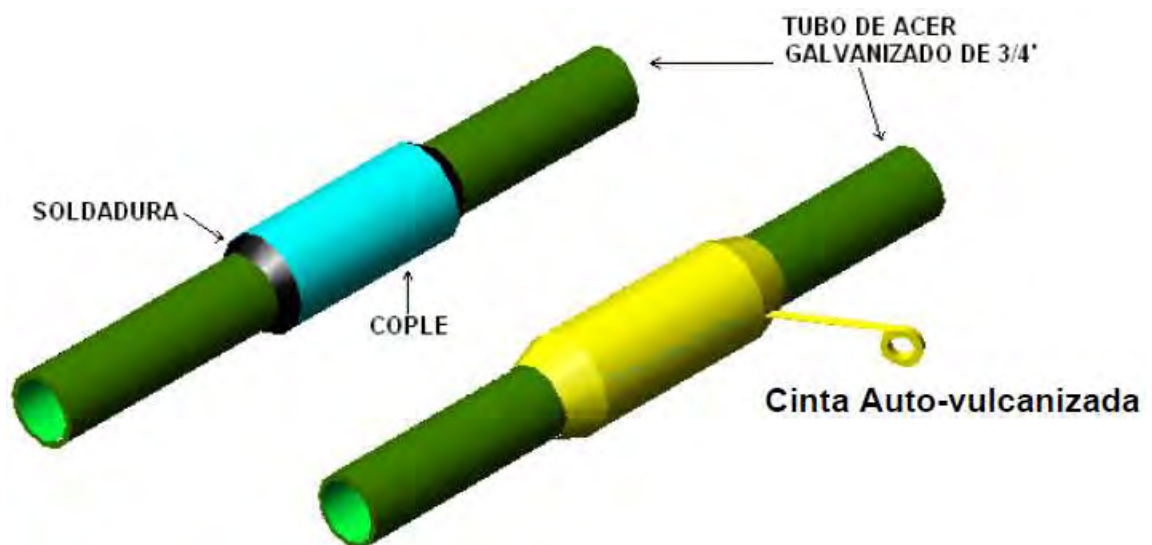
Unión de los tubos de acero galvanizado y aplicación de soldadura.
